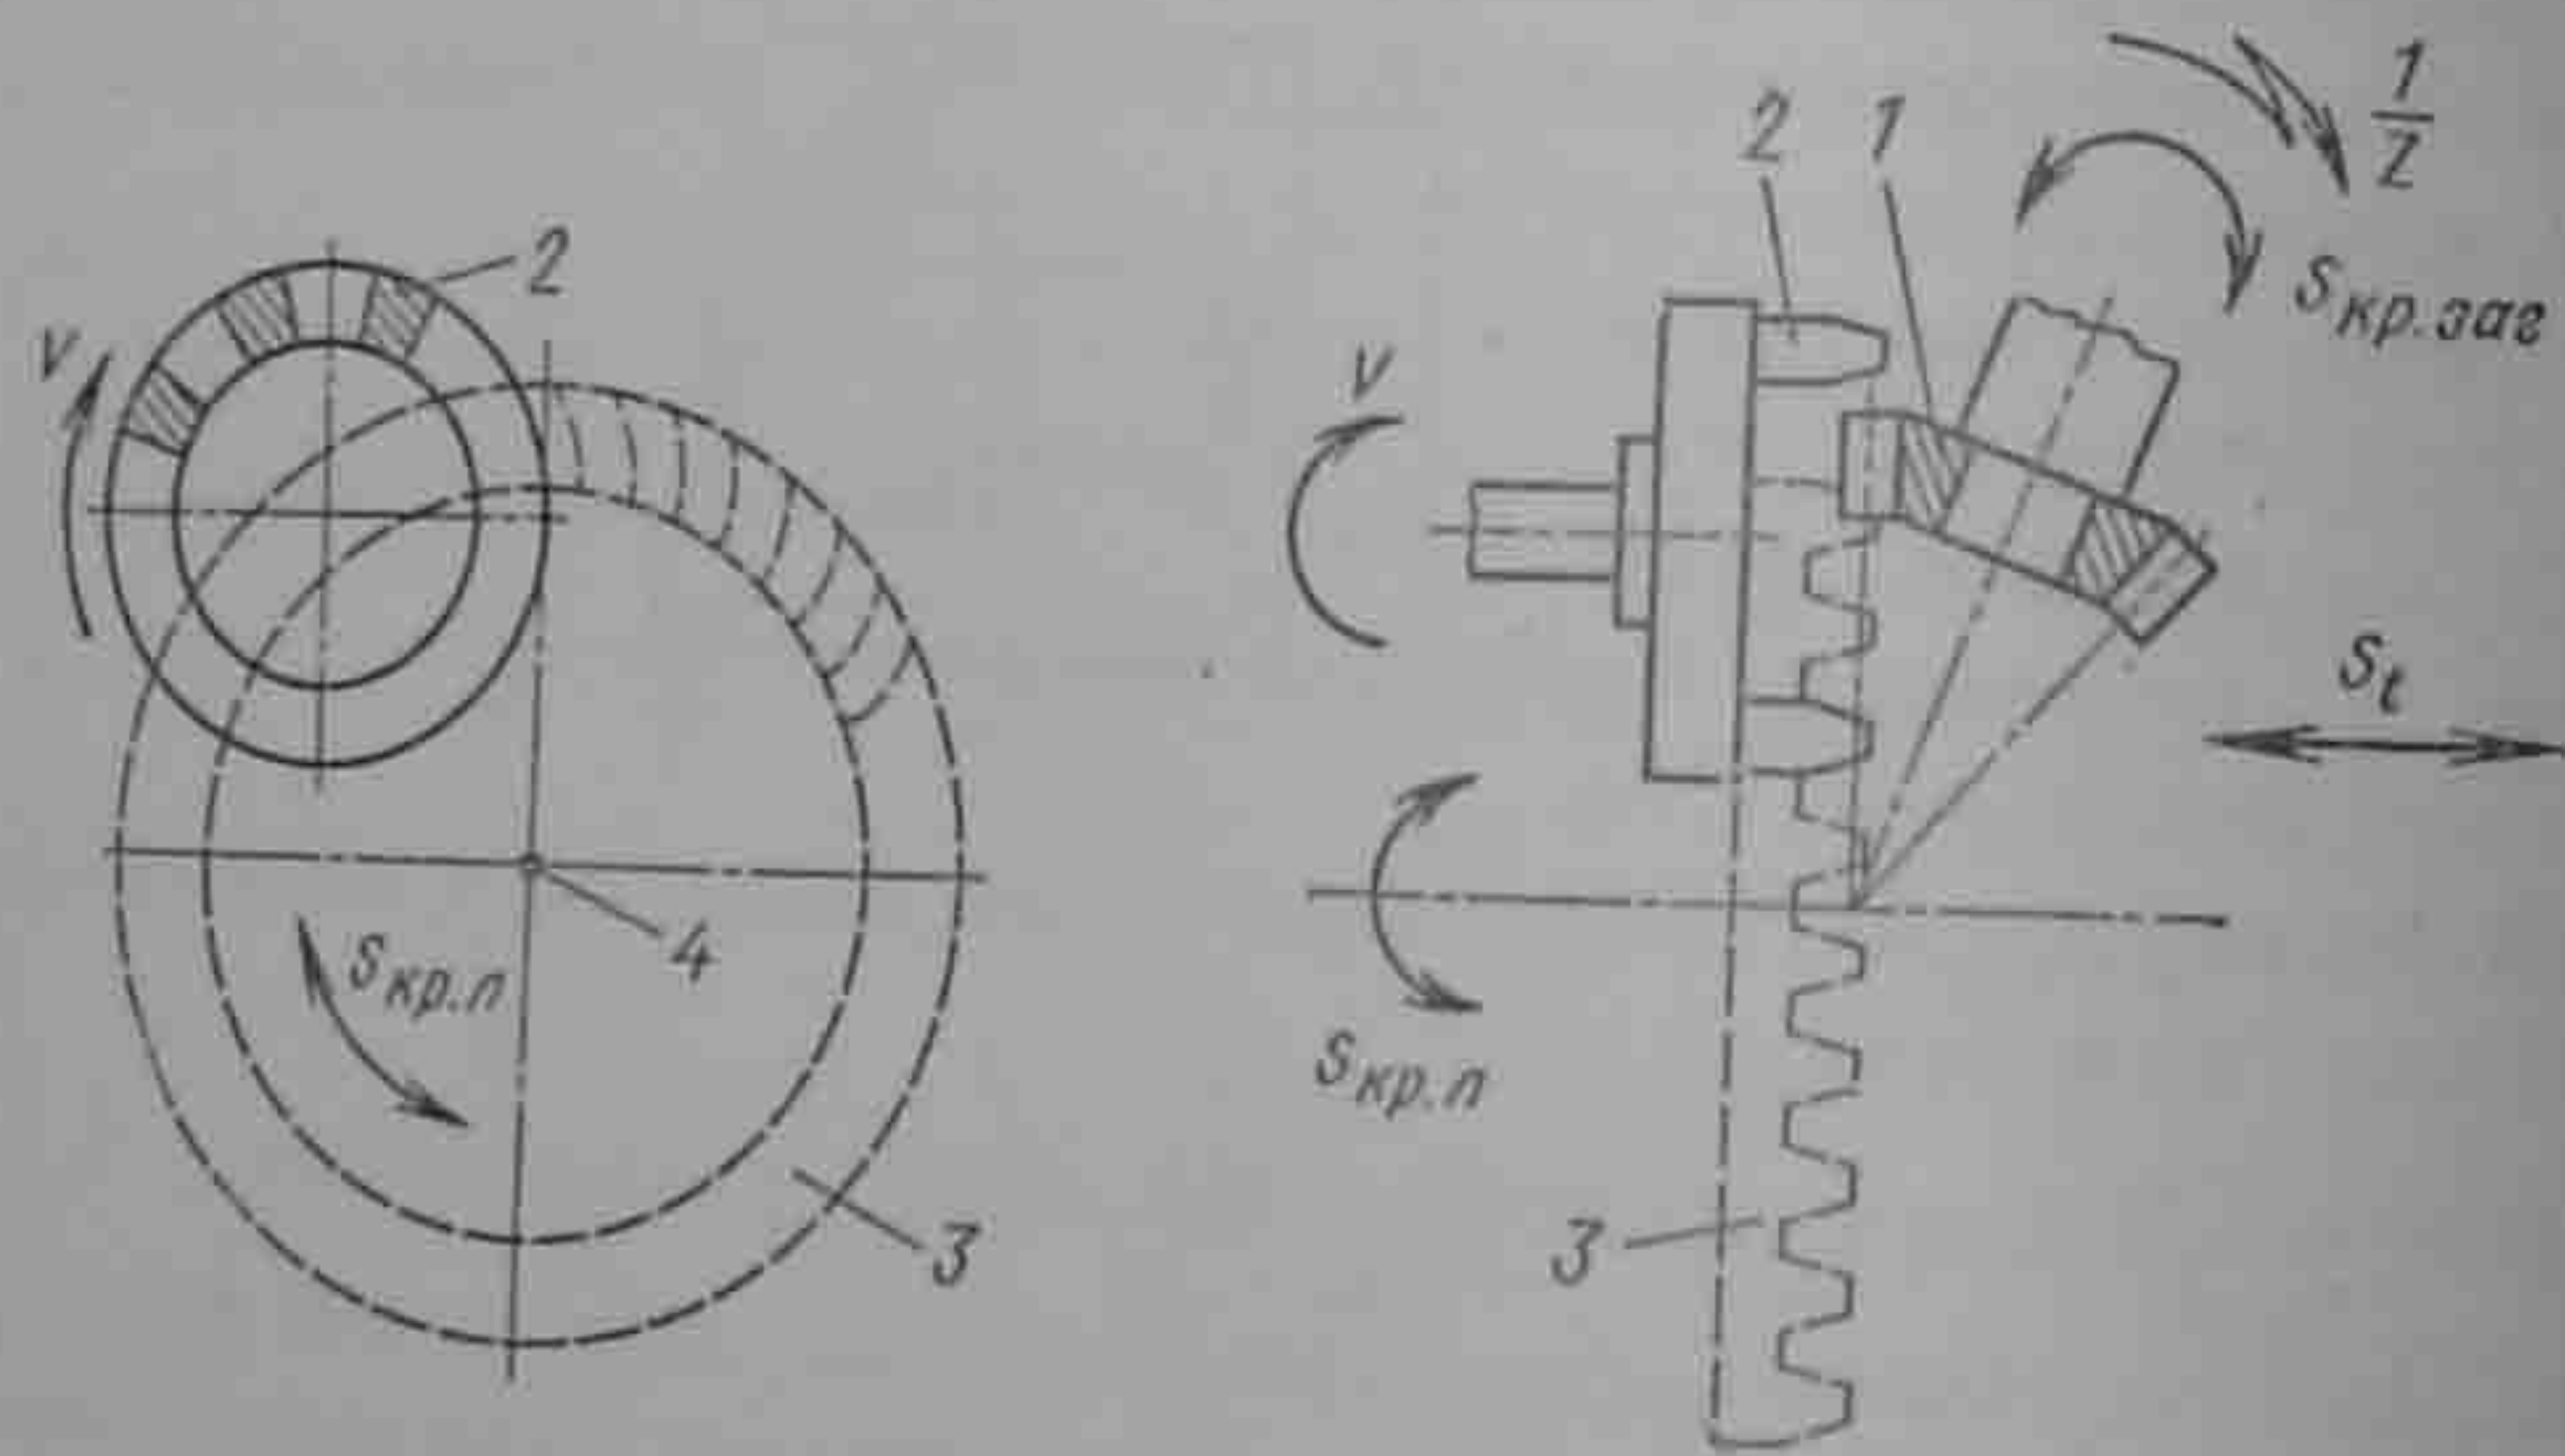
Схема нарезания конического колеса с круговыми зубьями
